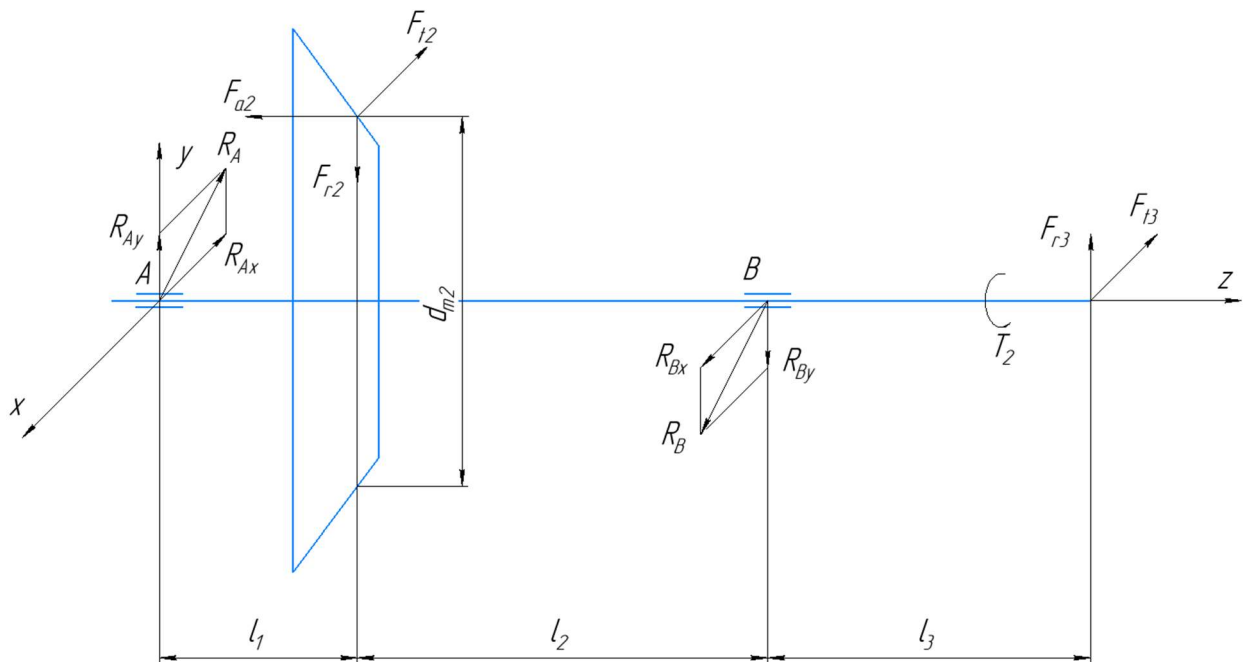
Схема нагружения подшипников тихоходного вала.
